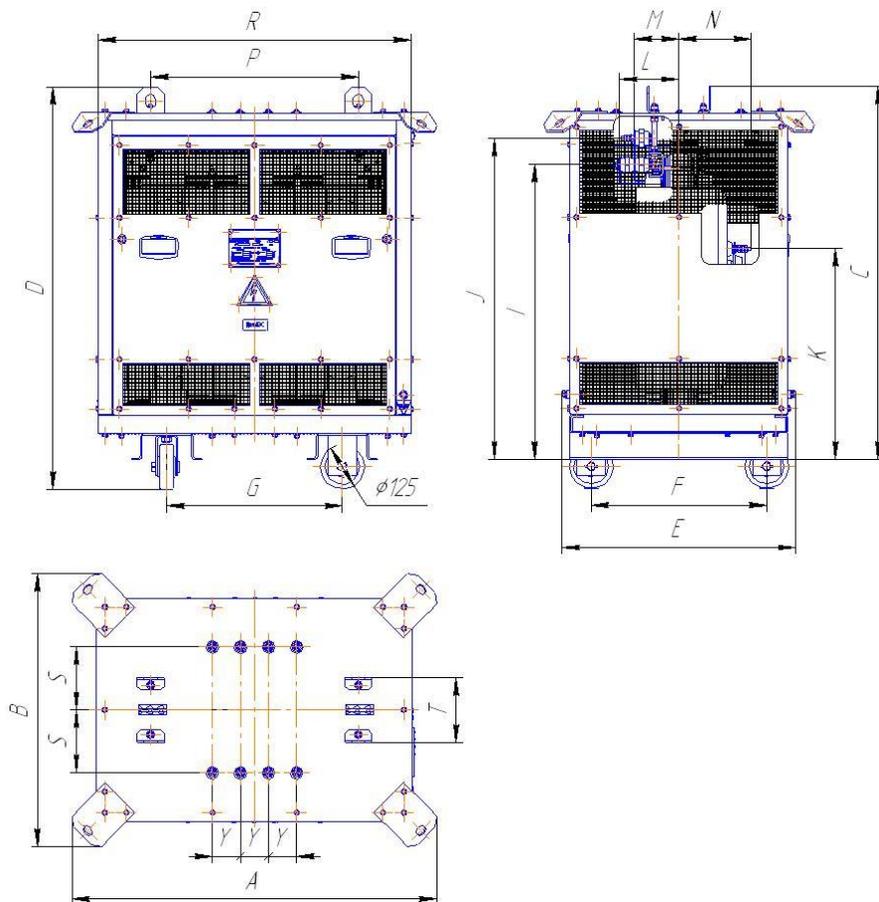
Габаритные, установочные и присоединительные размеры трансформатора со степенью защиты IP21 (в кожухе).
